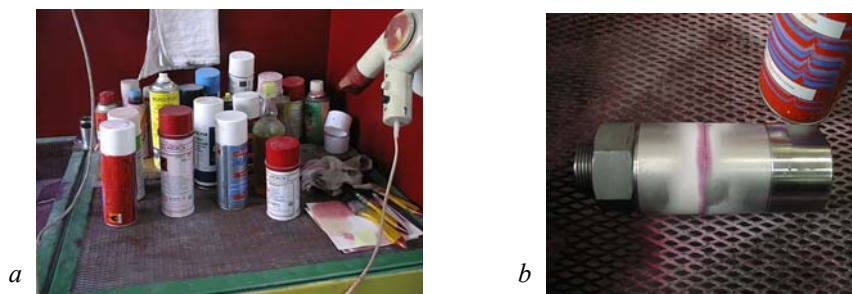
Lichide penetrante (*a*) și etalonul Miller (*b*).
